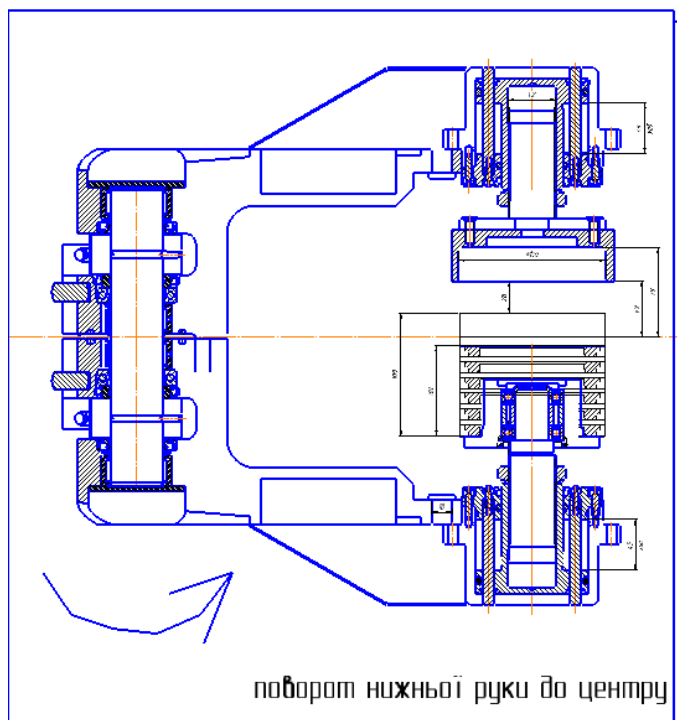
Поворот нижньої руки маніпулятора з обробленими по зовнішній поверхні заготовками до правого шинделя
